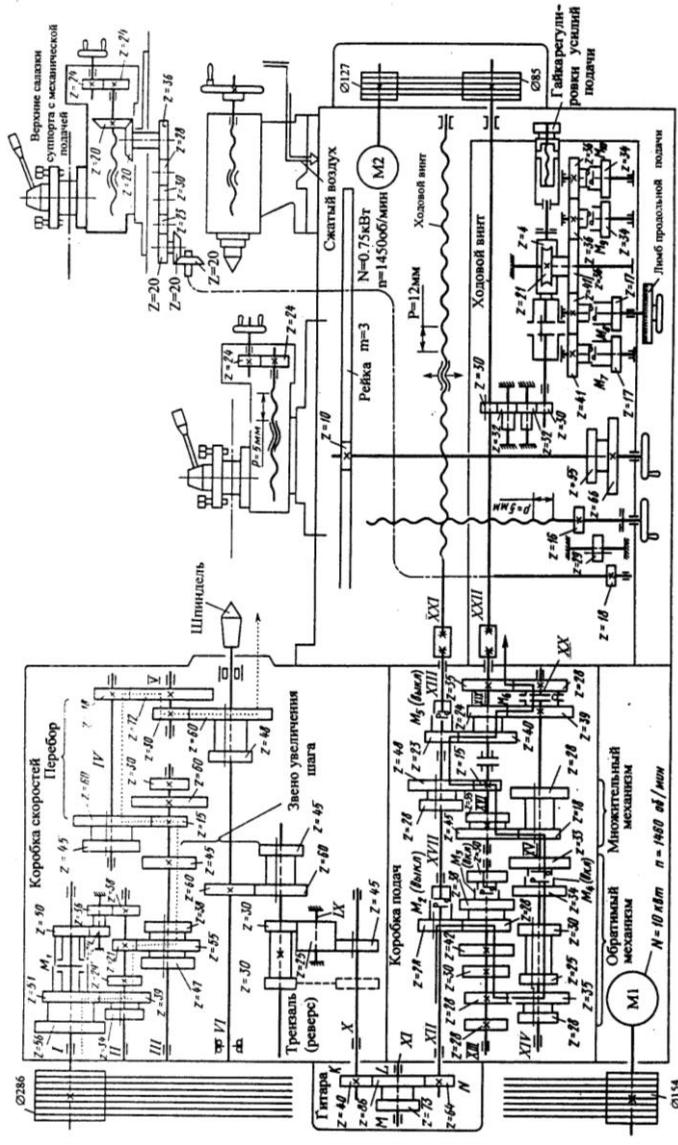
Кинематическая схема токарно-винторезного станка модели 16К20
